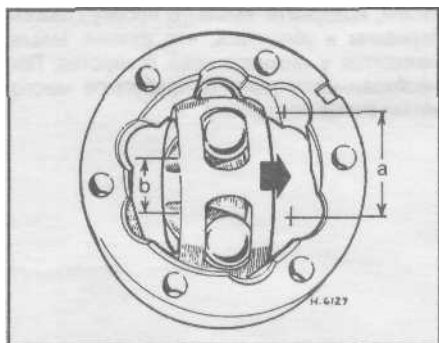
Установка сепаратора и ступицы внутреннего шарнира в корпус "а" следует ориентировать относительно "в"
